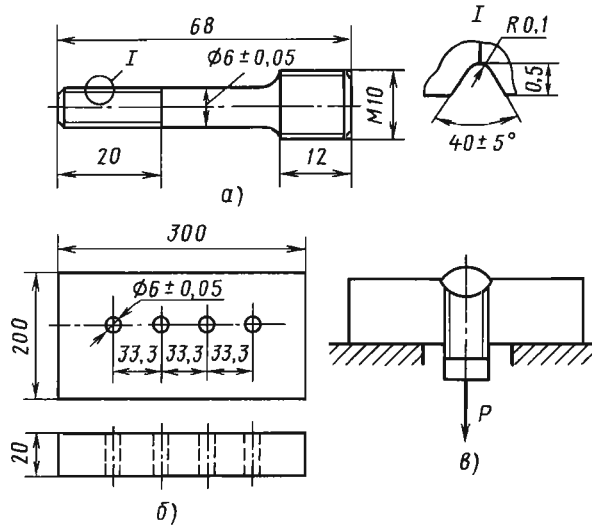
Образец-вставка (а), пластина под сварку (б) и схема нагружения образца (в) по методу «Импланта»
